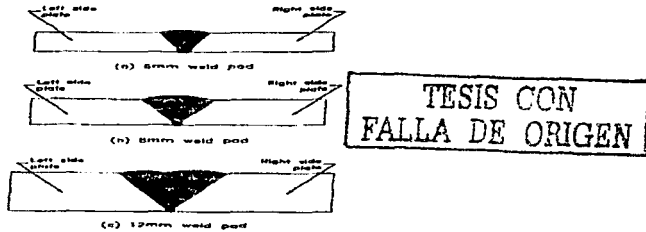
Secuencia de los cordones de soldadura en placas con espesor de 6, 8 y 12 mm [84].
